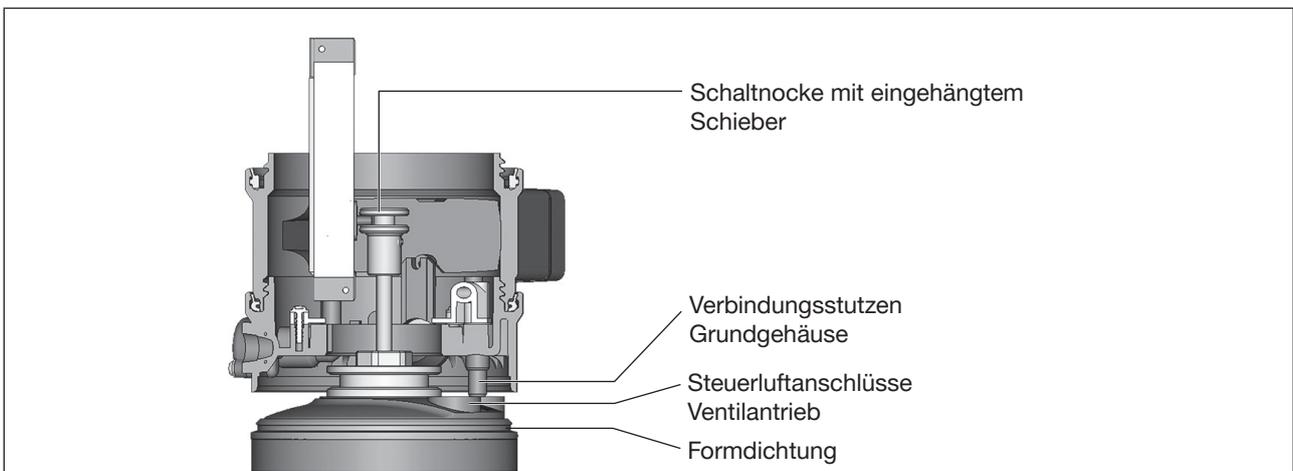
Wegaufnehmer zum Antrieb ausrichten
